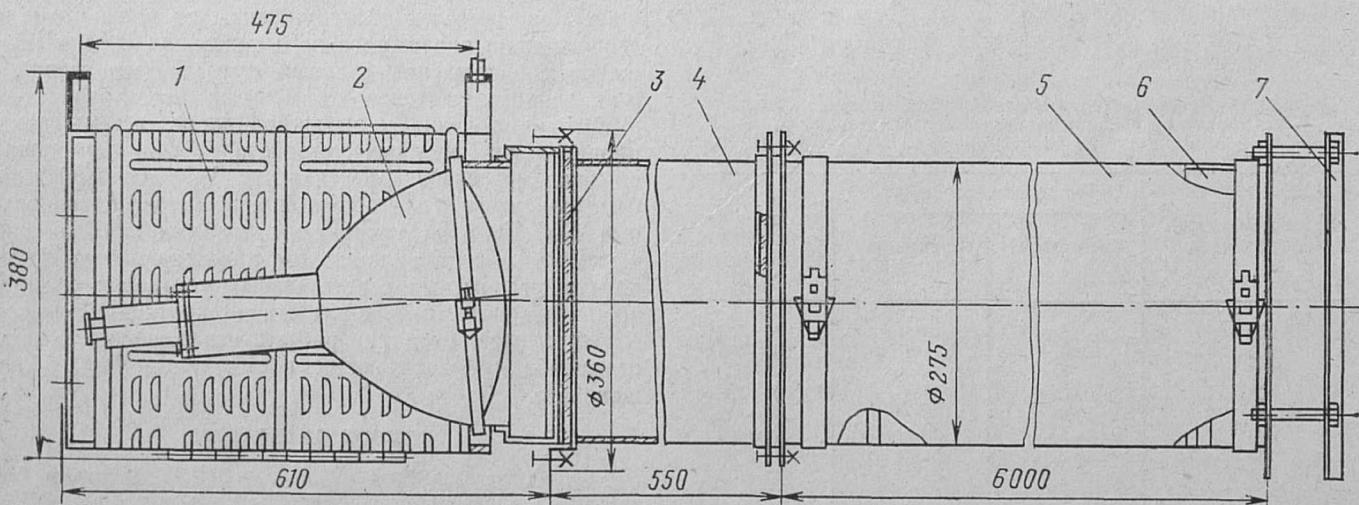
Чертеж общего вида КОУ1А-М275-1×700.
